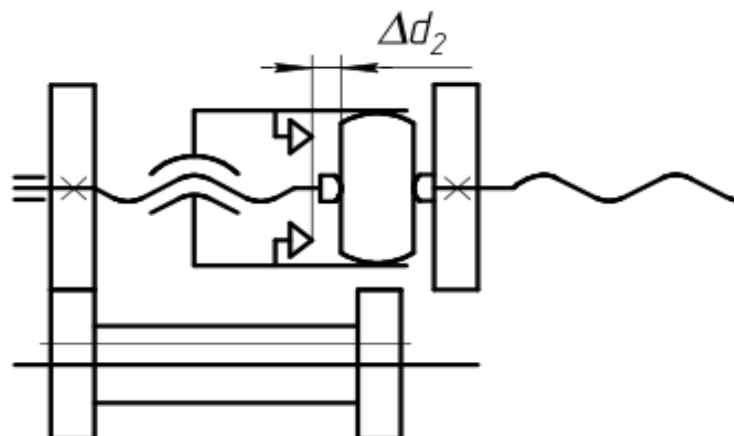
Схема настройки станка на величину снимаемого припуска.
